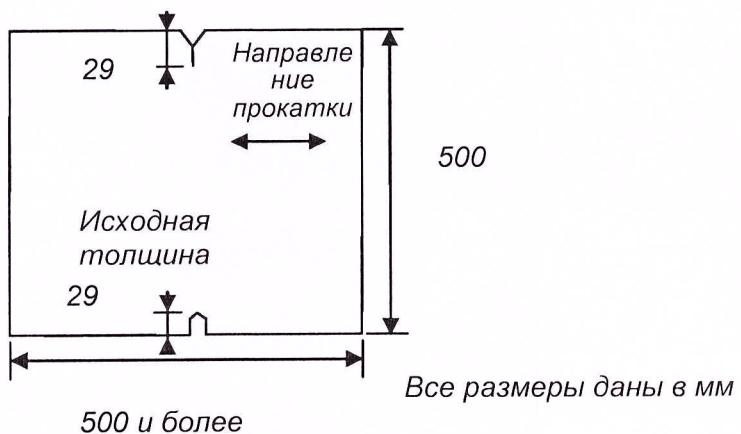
Форма и размер испытываемого образца
